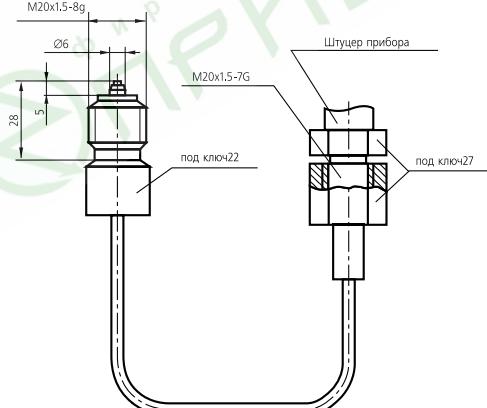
Рукав соединительный гибкий. Габаритные и присоединительные размеры
